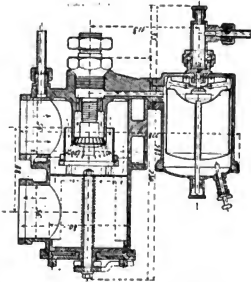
Longemare-Karburator B 18 für 1 1/4 pferdige Motore.
